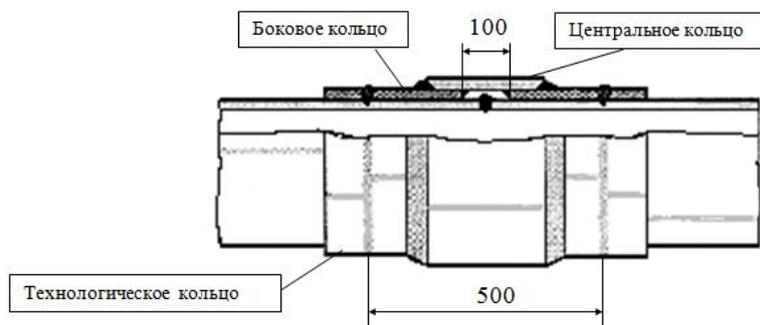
Муфта типа П5 сварная галтельная с технологическими кольцами для ремонта сварных кольцевых швов
